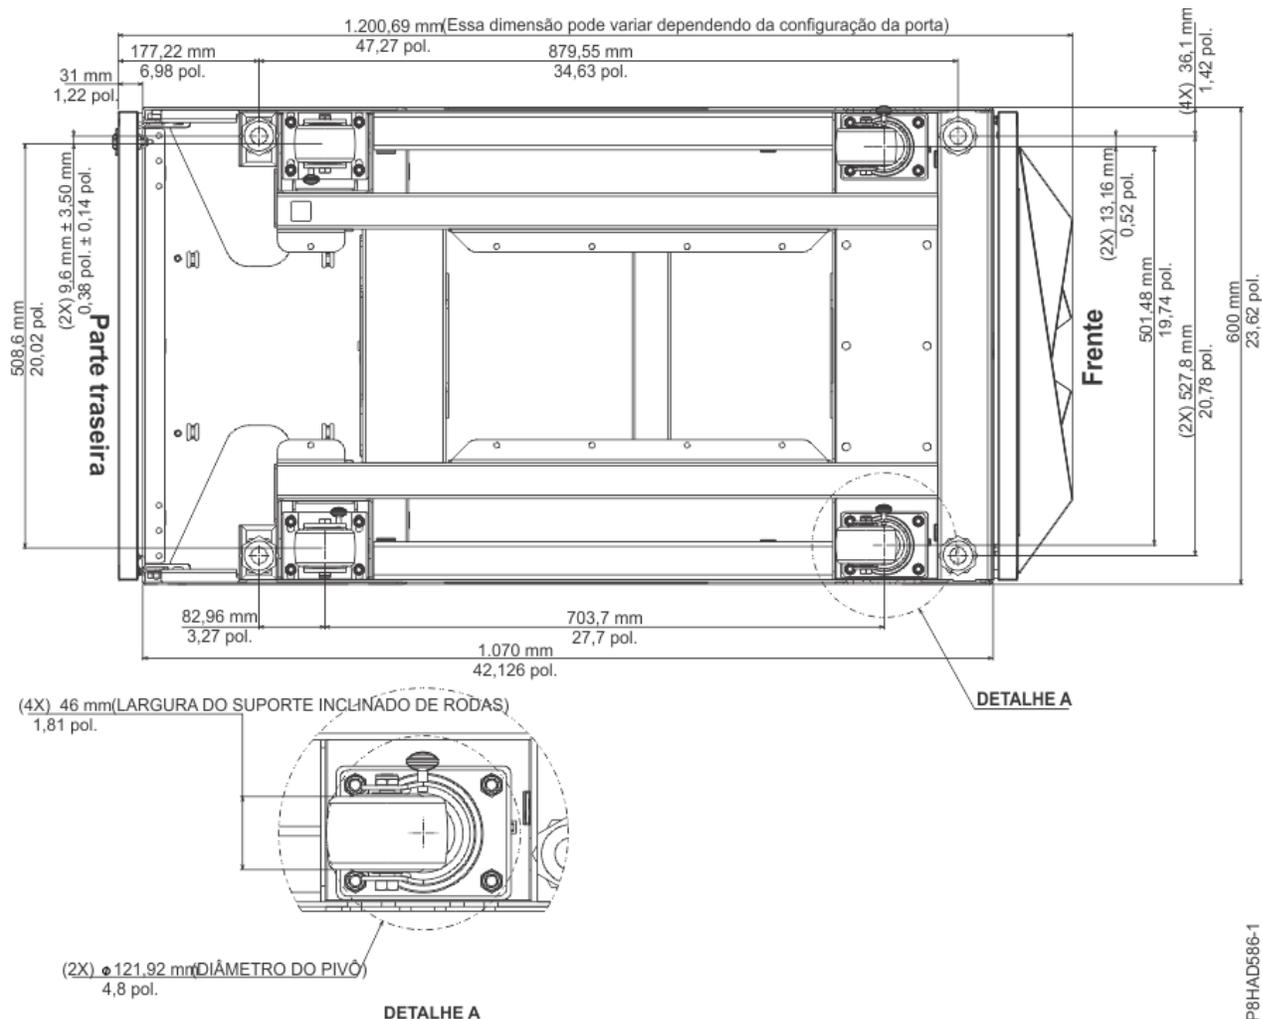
Locais do suporte inclinado de rodas e do nivelador
